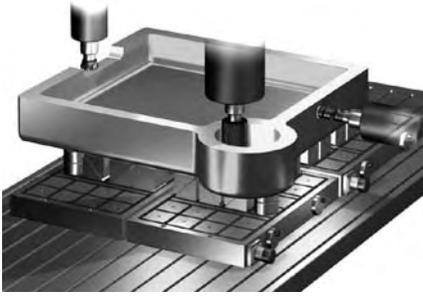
Aplanado y contorneado de piezas fundidas y moldeadas
